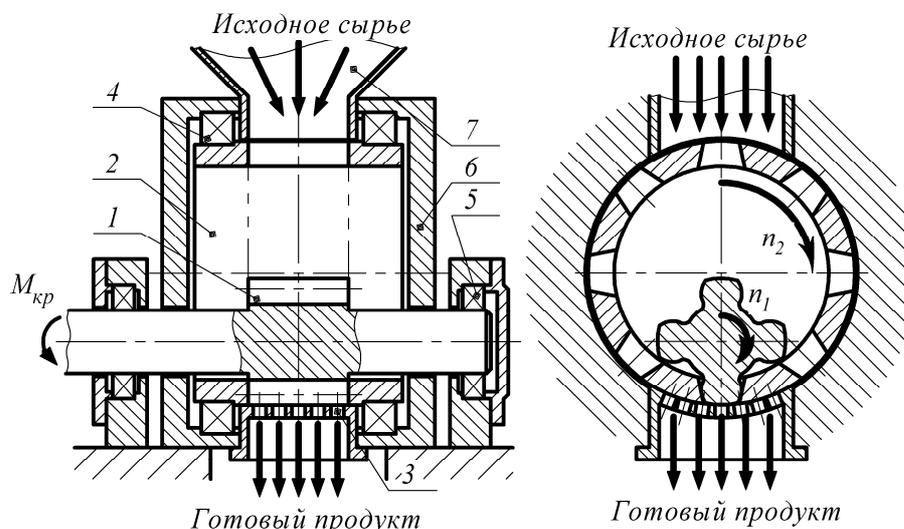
Универсальный измельчитель цилиндрического зацепления ИЦЗ-08
